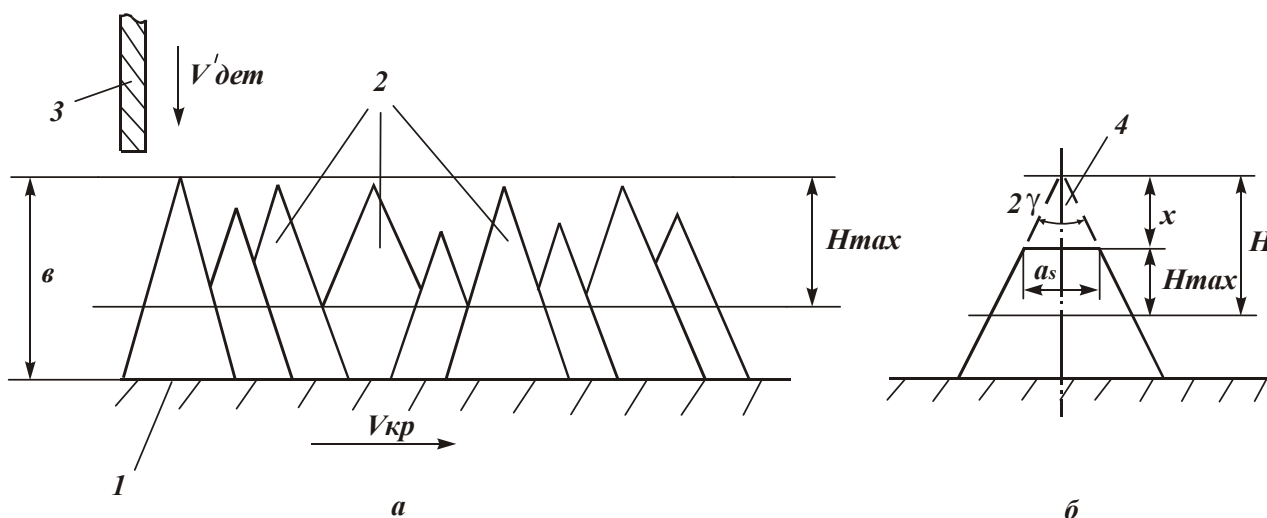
Расчетные схемы шлифования: 1 – связка круга; 2 – режущие зерна; 3 – обрабатываемая пластинка; 4 – изношенная часть зерна.
